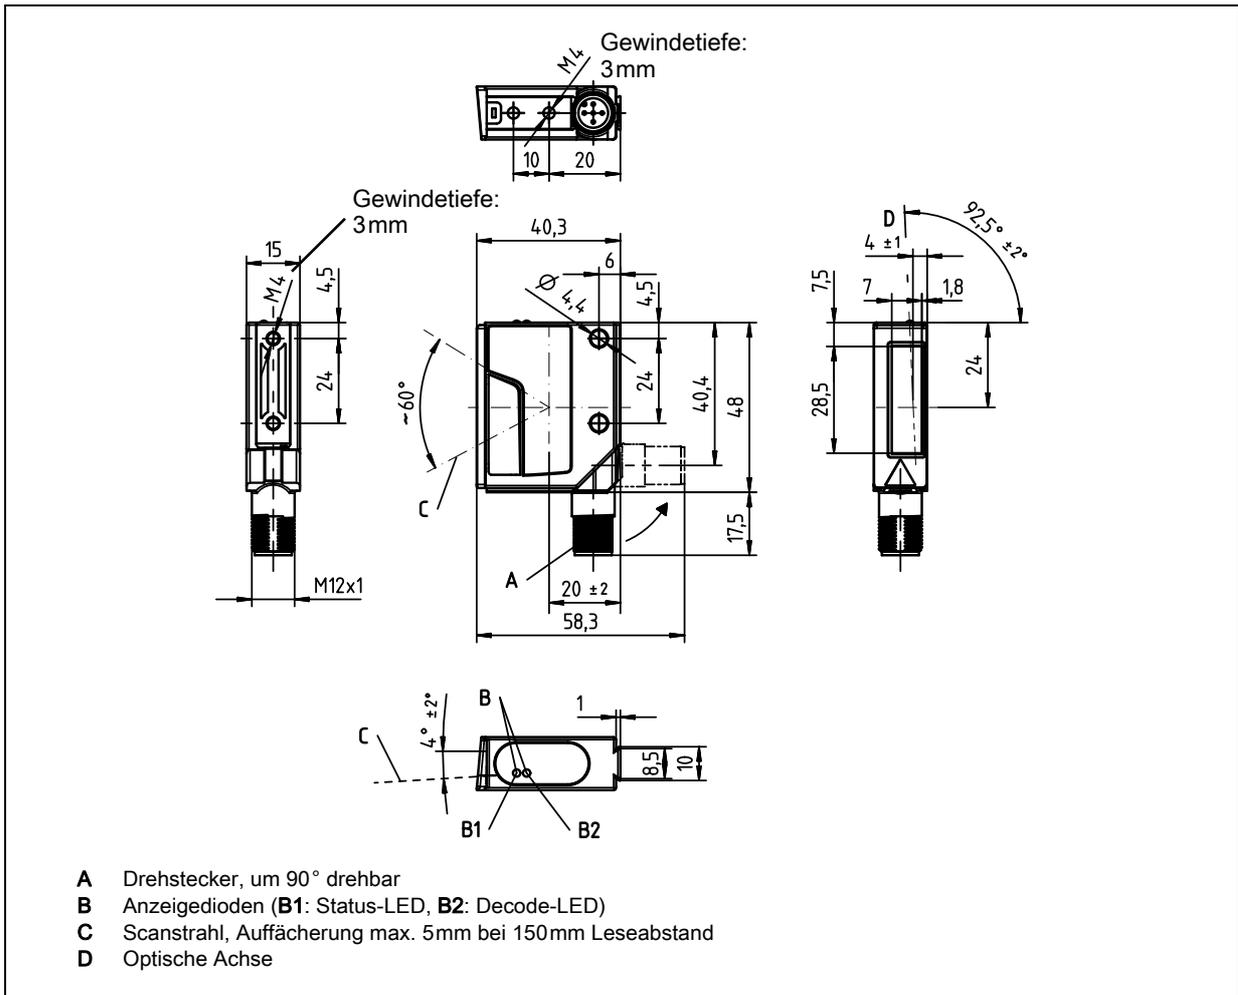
Maßzeichnung BCL 8 S M ...2, BCL 8 S N ...2 mit frontseitigem Strahlaustritt
